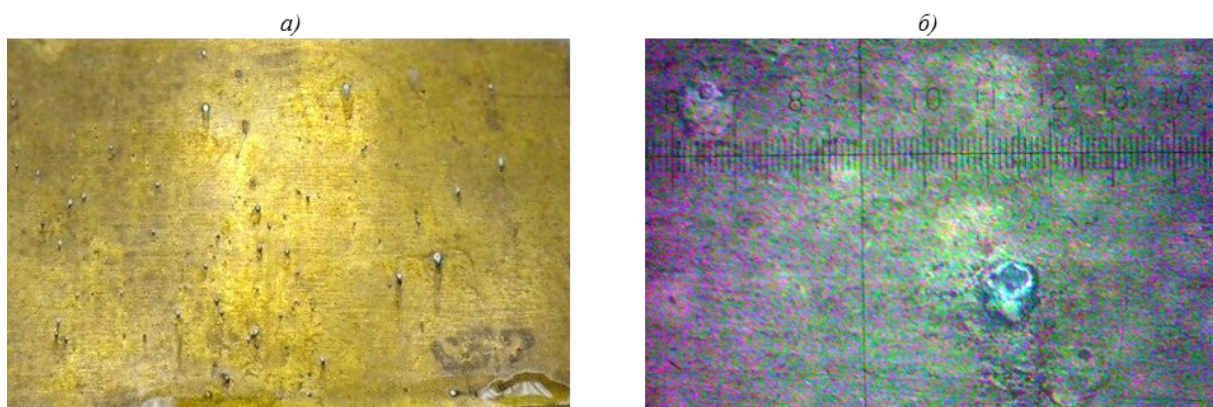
Внешний вид образца из пассивированной бронзы БрАЖ9-2 (а) и с коррозионным очагом на образце (б – $\times 8$)
